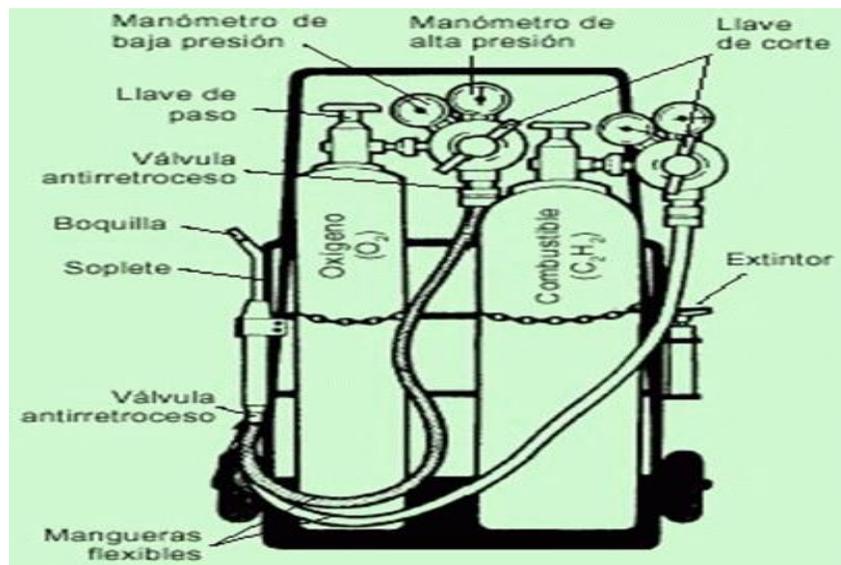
Partes de la soldadura acetilénica.
